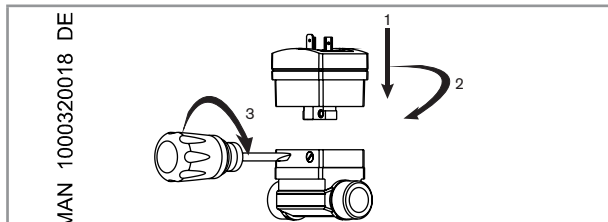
Montage des SE30 HT und des Sensor-Fittings S030 HT
